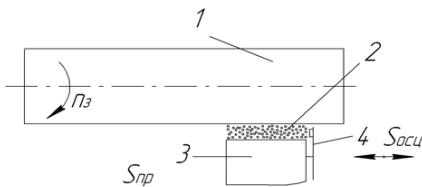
Схема магнитно-абразивной обработки с наложением ультразвуковых колебаний: 1 – обрабатываемая деталь; 2 – ферромагнитный порошок; 3 – полюсный наконечник; 4 – пружинная пластина
